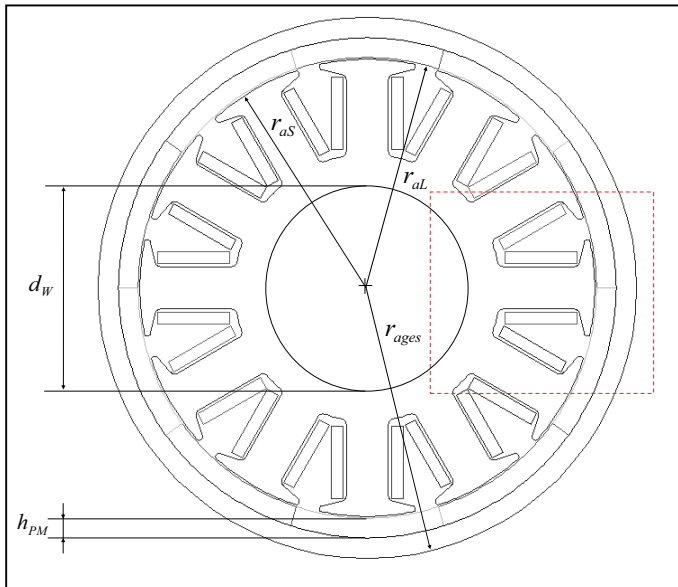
Querschnitt eines zehnpoligen Außenläufermotors mit genutetem Ständer. Die relevanten Abmessungen sind eingezeichnet.
